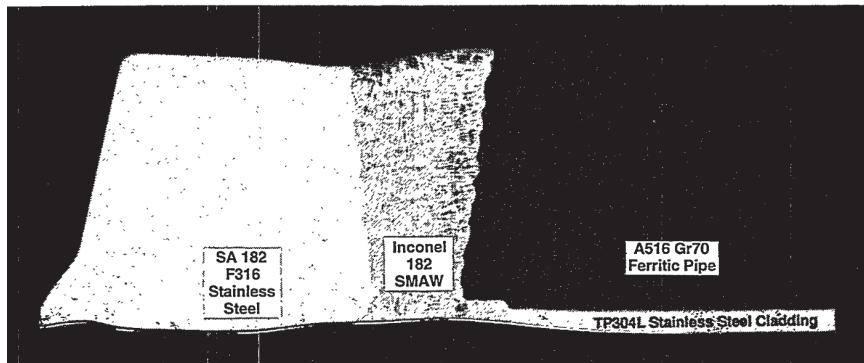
Soudure bimétallique du projet NRC
